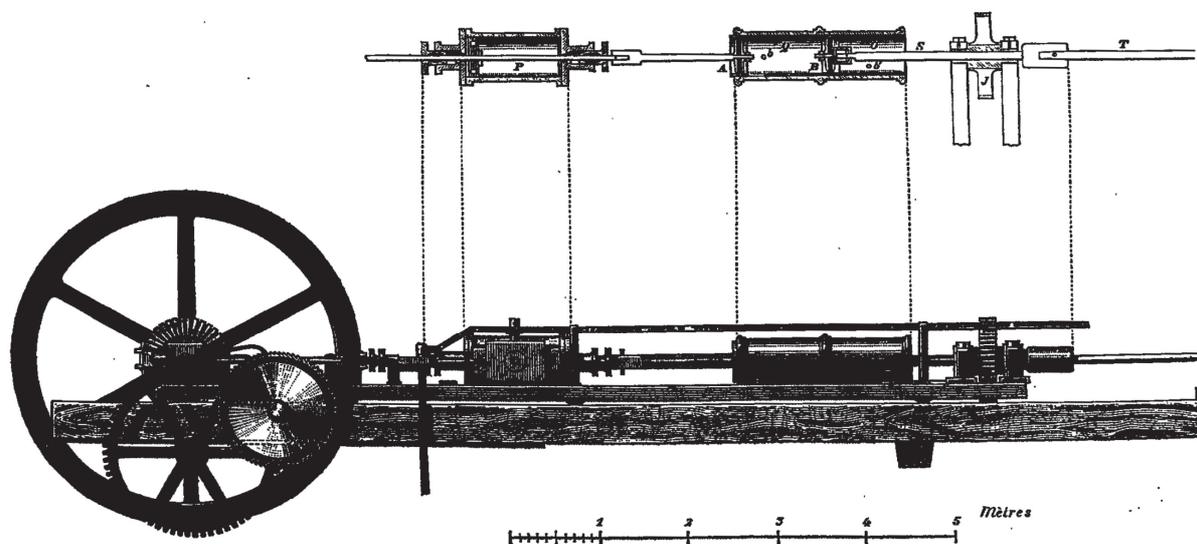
LA MACHINE PERFORATRICE BARTLETT, A VAPEUR ET A AIR COMPRIMÉ
